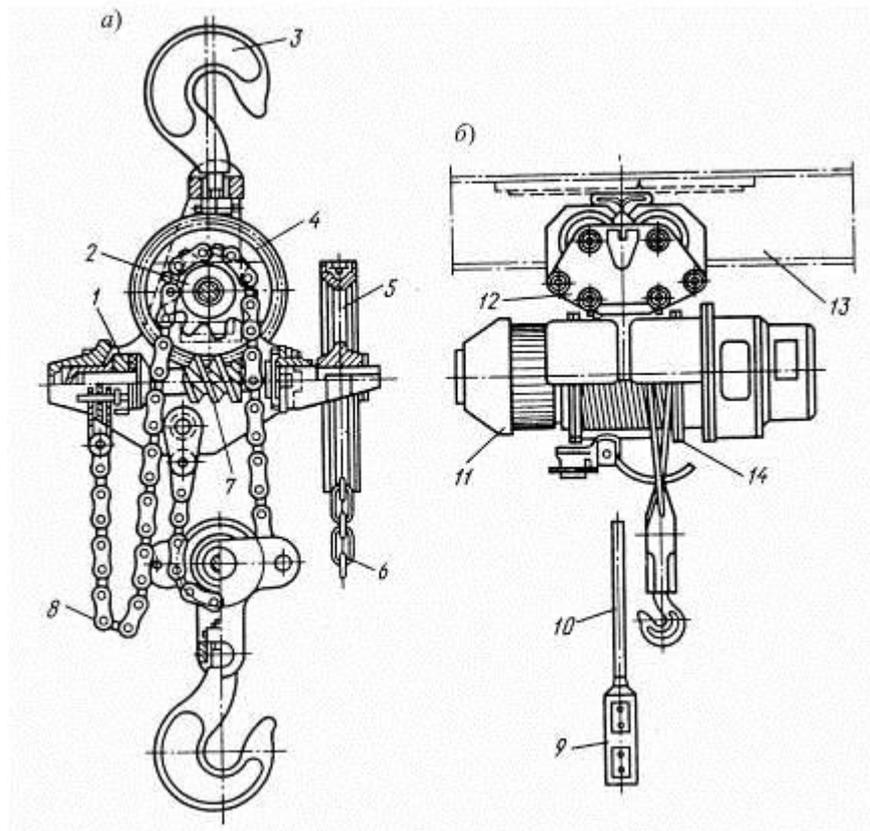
Таль (а) и тельфер (б): 1 — тормоз; 2 — звездочка; 3 — крюк, 4 — червячное колесо; 5 — цепное колесо; 6 — приводная цепь; 7 — червяк; 8 — тяговая цепь; 9 — пульт управления; 10 — гибкий кабель; 11 — электродвигатель; 12 — тележка; 13 — монорельсовый путь; 14 — канатный барабан
